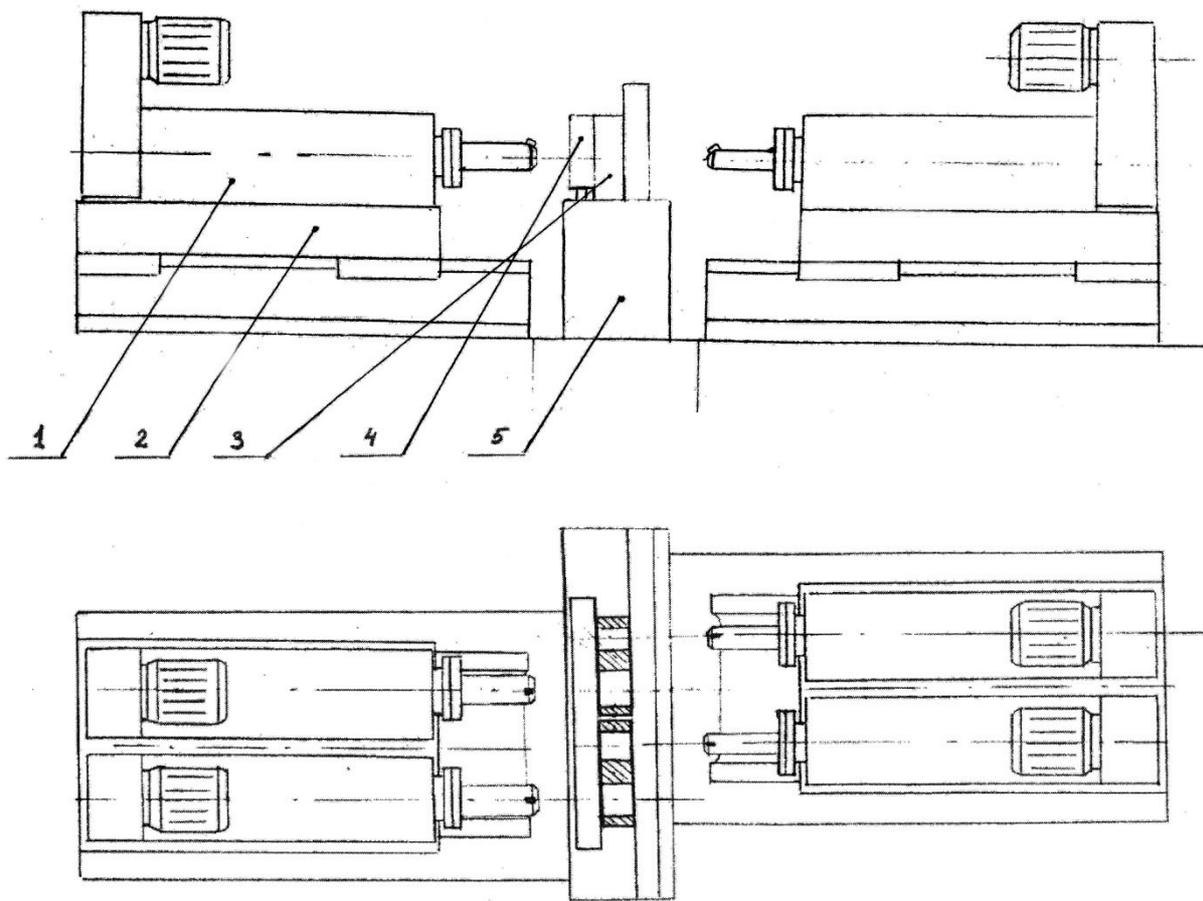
Схема обработки деталей на агрегатно-расточном станке:
